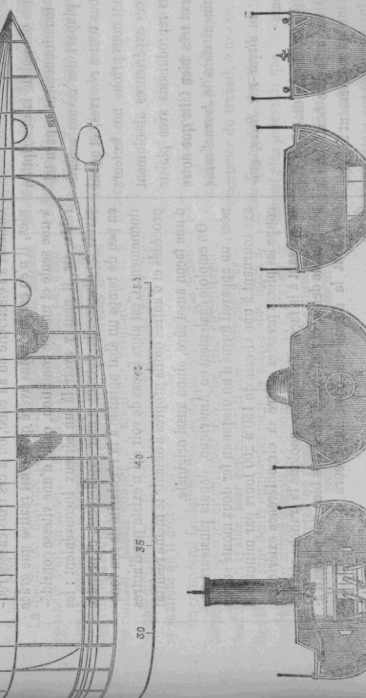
Sectiones verticales et transversales du torpilleur l'Achéron.
